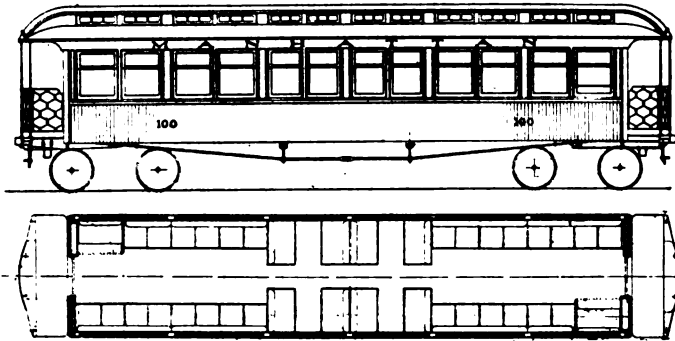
Automotrice du Manhattan Railway. Plan et élévation.
